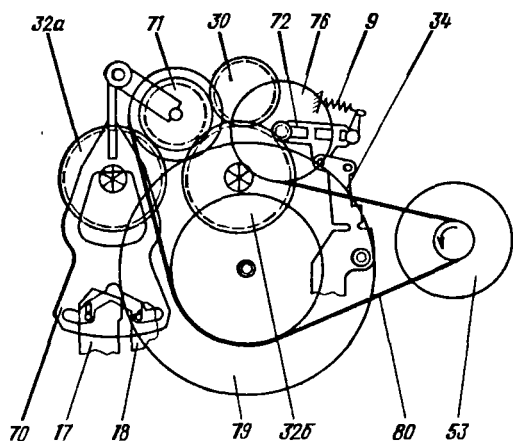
Кинематическая схема ЛПМ типа КМ-III. (Позиционные обозначения даны по каталогу): 9 — пружина муфты сцепления; 17 — рычаг обратной перемотки; 18 — рычаг прямой перемотки; 30 — промежуточная шестерня; 32a — подающий шпindel; 32b — приемный шпindel; 34 — пластина прижимного ролика; 53 — двигатель; 70 — рычаг перемотки; 71 — шестерня перемотки; 72 — рычаг муфты сцепления; 76 — диск муфты сцепления; 79 — маховик; 80 — пассив
